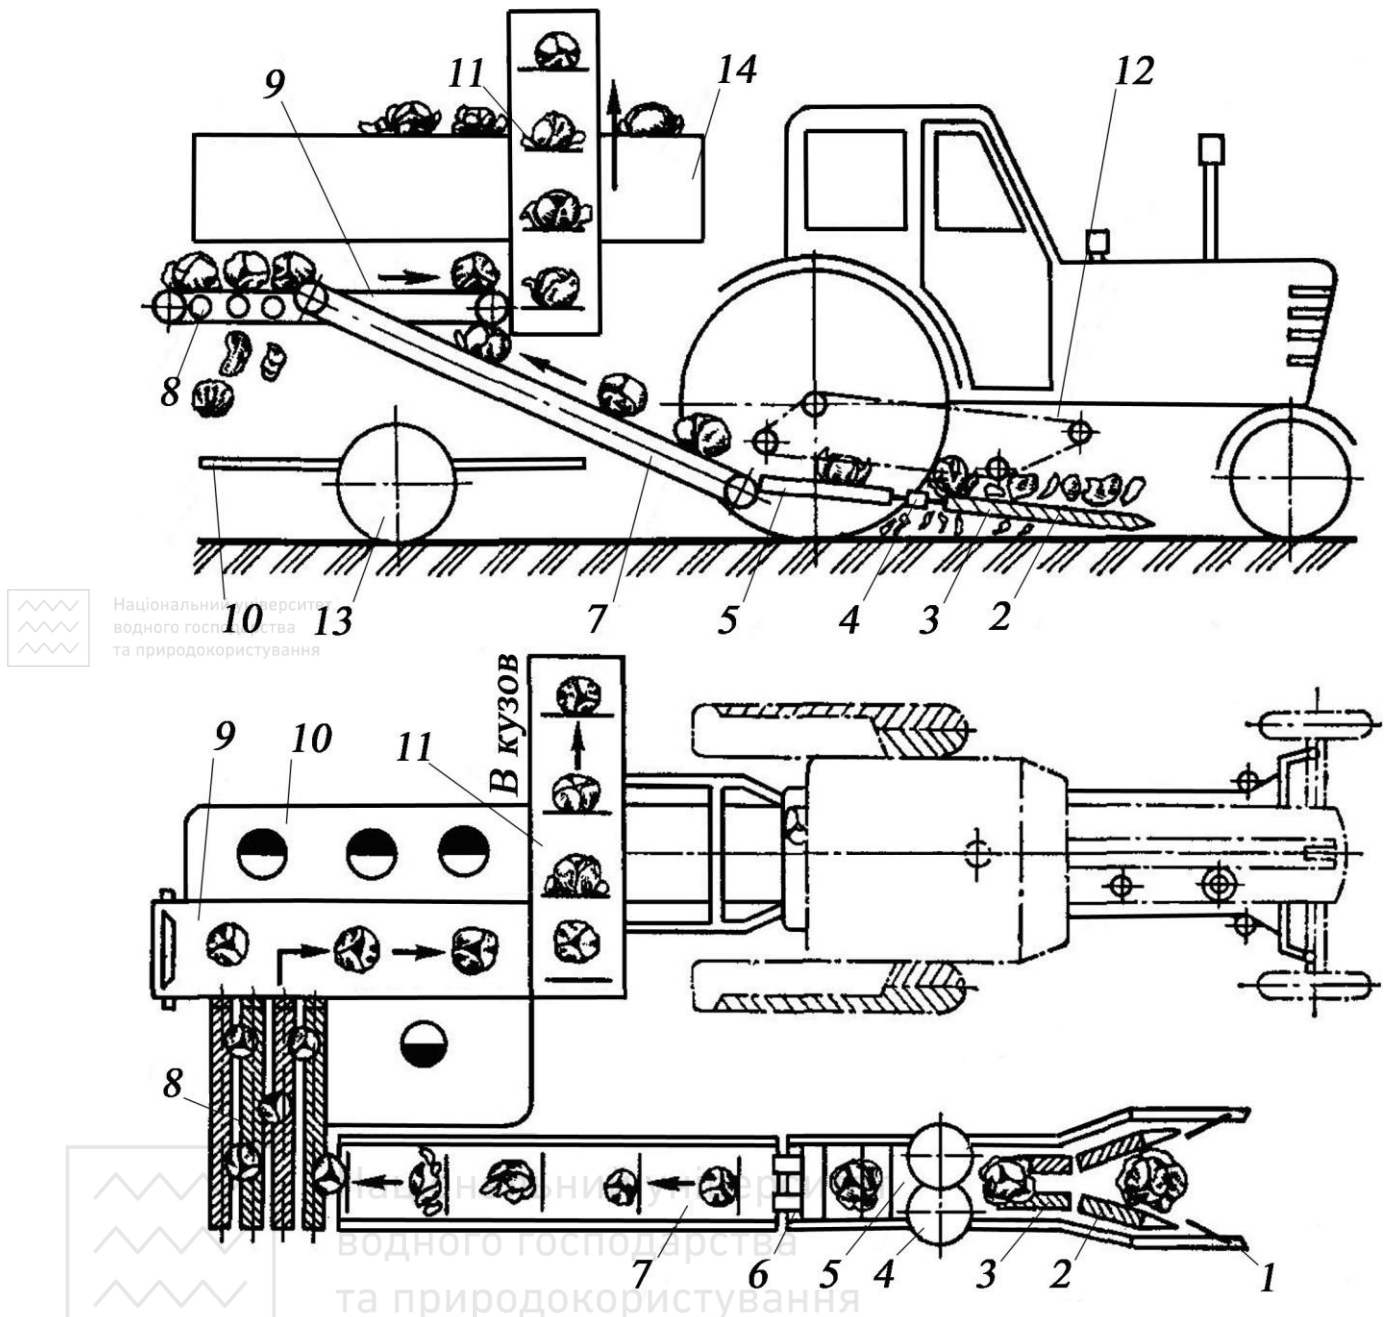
Комбайн для збирання капусти МСК-1: 1 - опорна лижа; 2 - конусні ліфтери із спрямовуючими шнеками; 3 - вирівнювальні шнеки; 4 - дискові ножі; 5 - потік; 6 - шарнірне кріплення зрізувального апарата; 7 - підйомний елеватор; 8 - гвинтовий листовідокремлювач; 9 - перебиральний транспортер; 10 - площадка для працівників; 11 - навантажувальний елеватор; 12 - транспортер; 13 - ходове колесо; 14 - транспортний засіб.
